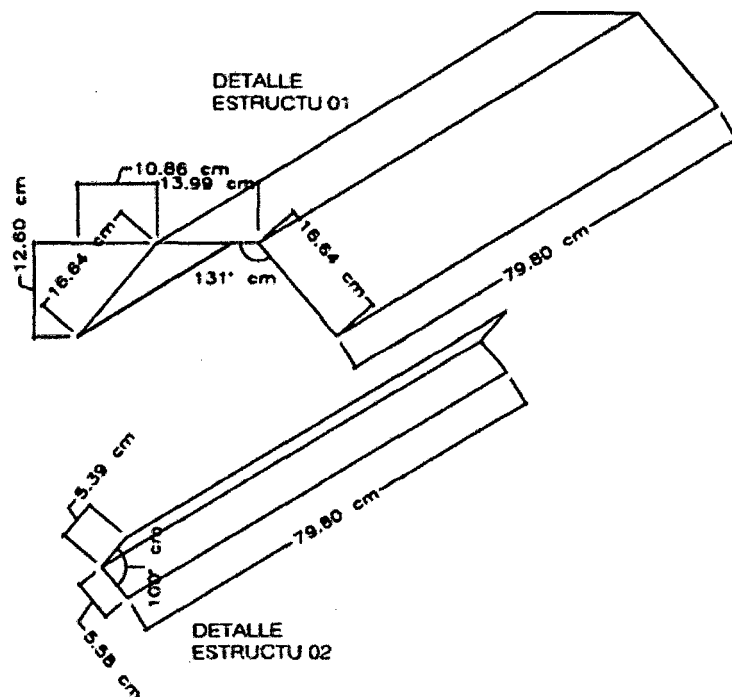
Detalles constructivos: Detalle de Estructura 01: Cámara separadora de gases, Detalle de Estructura 02: Deflector.
